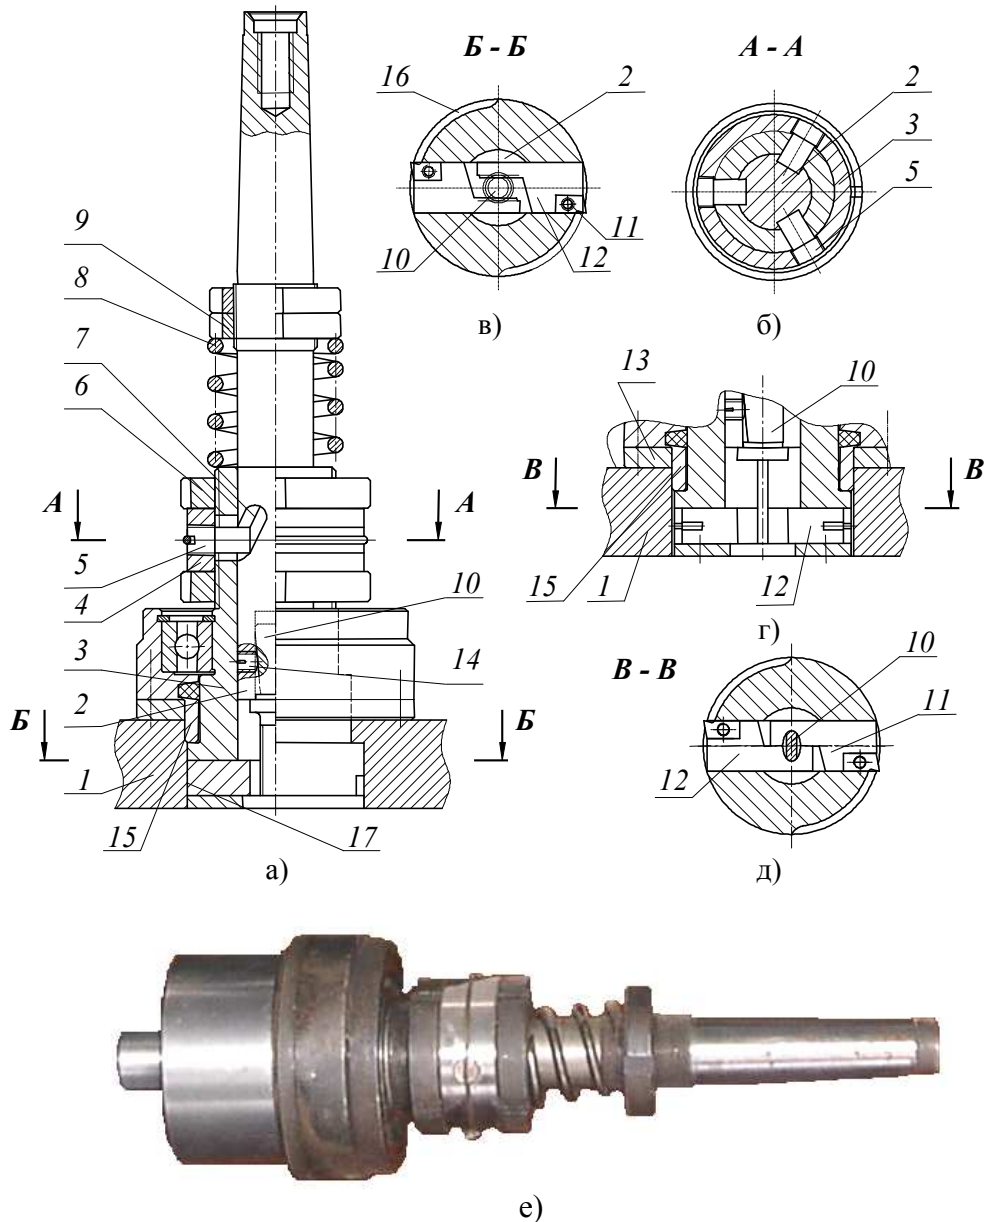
Пристрій для розточування кільцевих канавок в отворах корпусних деталей з використанням кінематичних зв'язків оправка-різець: а, б) рейкове з'єднання; в, г) еліпсо-кулачкове з'єднання; е) загальний вигляд головки; 1 – корпус головки; 2 – оправка; 3 – втулка; 4 втулка регульовальна; 5 – гвинти; 6 – гайка; 7 – байонетний паз; 8 – пружина; 9 – гайка і контргайка; 10 – зубчаста передача; 11 – різці; 12 – зубчасті рейки; 13 – регульовальна шайба; 14 – гвинт; 15 – центрувальний корпус
